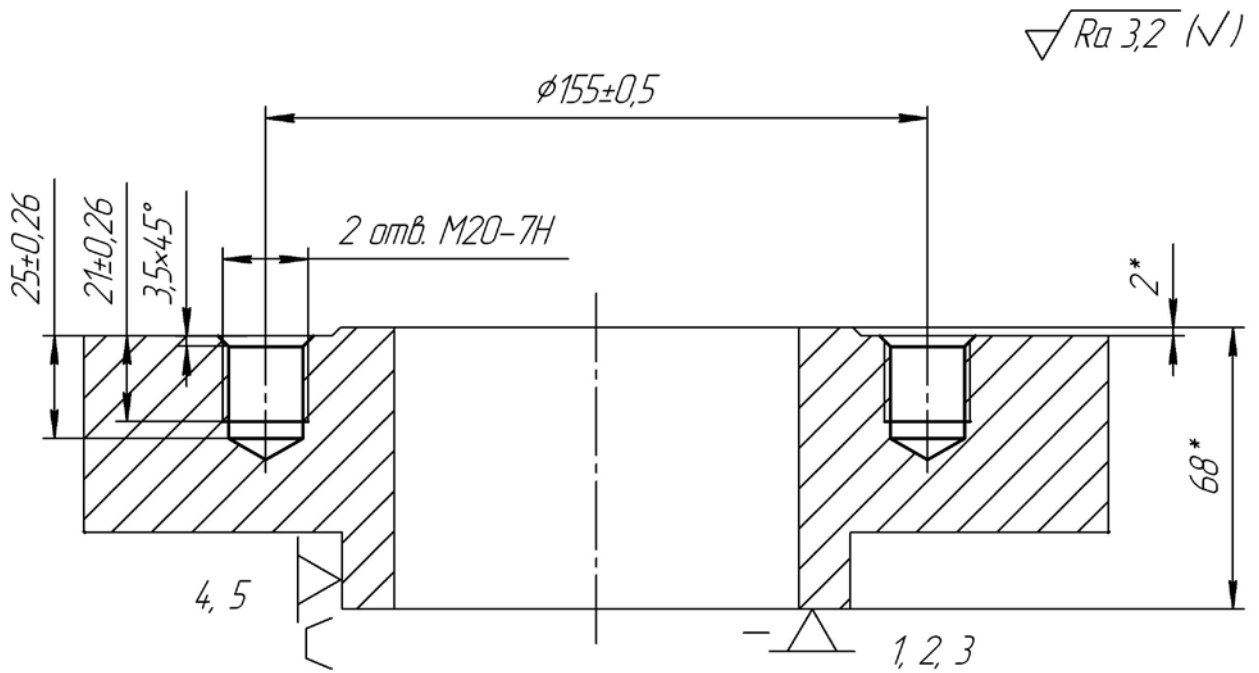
Схема базування заготовки на операції 025 свердлильній з ЧПК
